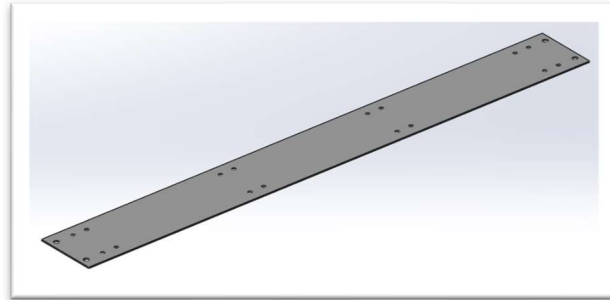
Soporte para 4 elevadores. Fuente: Elaboración propia
